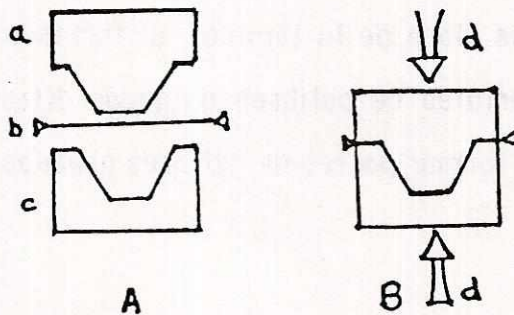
Moldeo por medio de molde hembra y molde macho. A: Lámina precalentada previo al formado. B: Lámina formada por medio de un movimiento simultáneo de dos moldes. a: Molde macho. b: Lámina precalentada y sujeta. c: Molde hembra. d: Fuerza aplicada.
